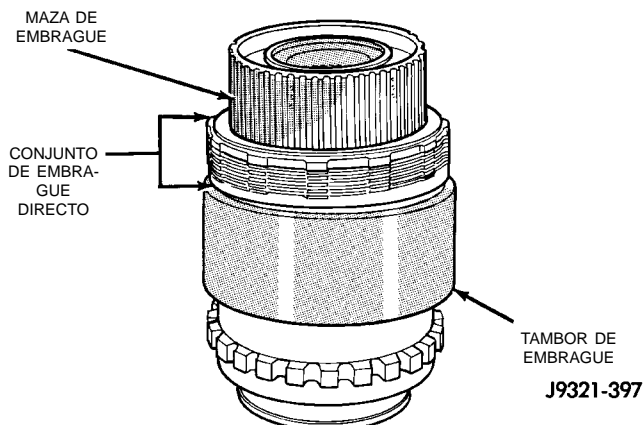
Instalación del conjunto de embrague directo y maza de embrague
